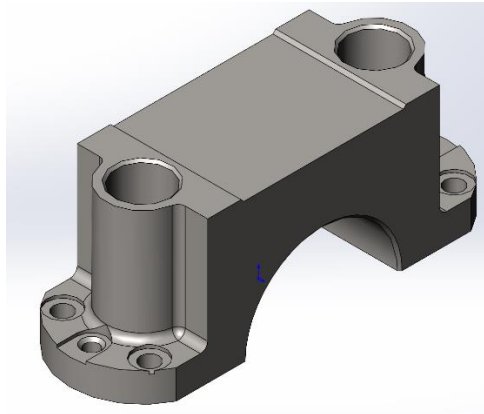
3Д-модель деталі “Корпус ПКУ.07.144”
